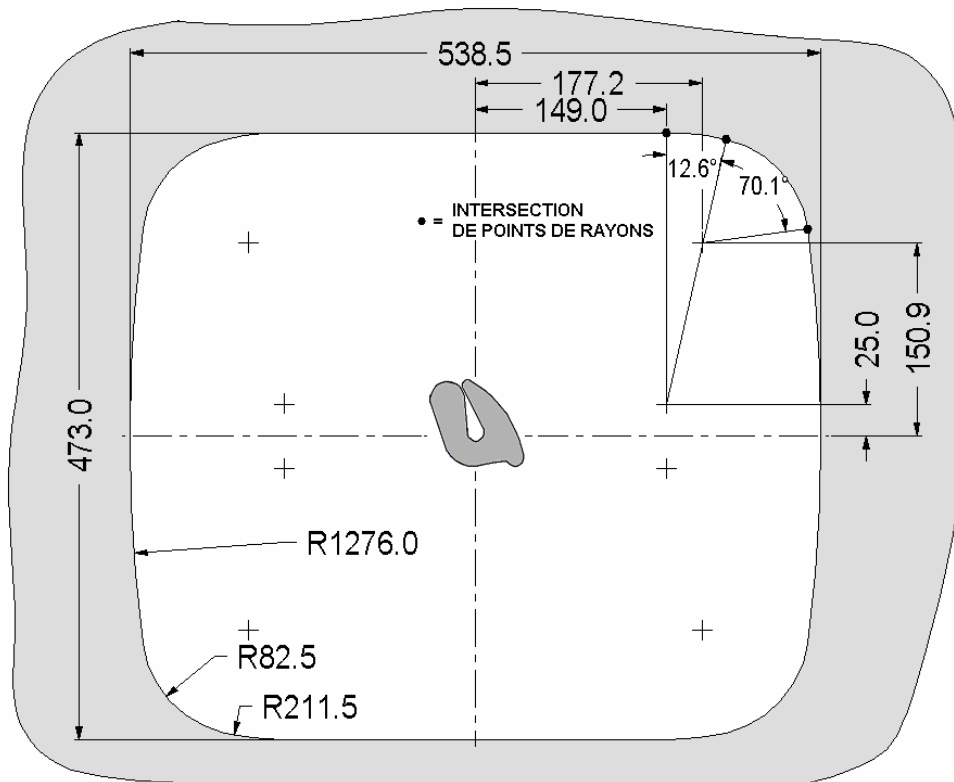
DETAILS CONCERNANT LA DECOUPE DU PLAN DE TRAVAIL
